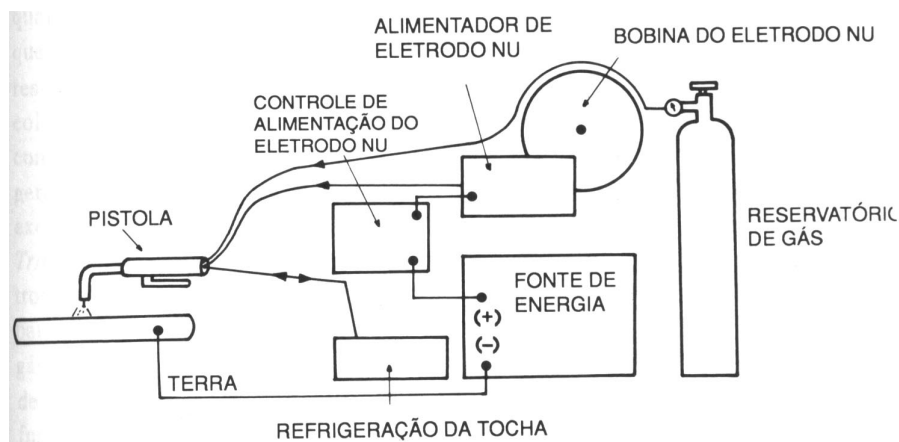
9 - Equipamento para soldagem MIG/MAG (Brandi, Wainer e Mello, 1992)
